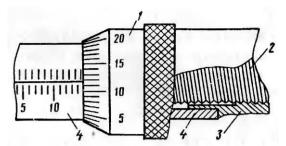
Барабан в разрезе: 1 — барабан; 2 — микровинт; 3 — резьбовая втулка; 4 — стебель
